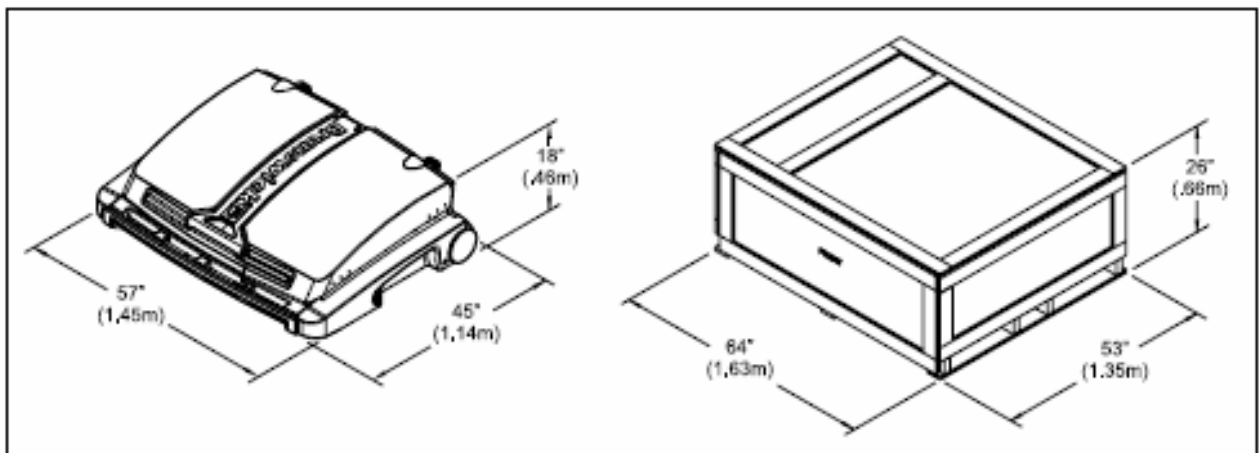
Dimensions de la machine et de la caisse d'emballage
